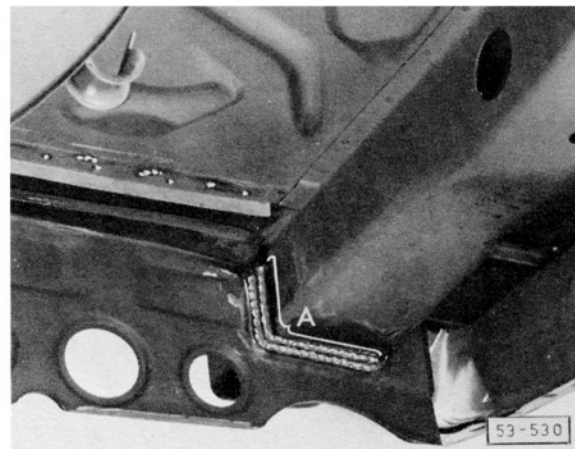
Stoßfängerhalter und Querträger am Abschlußblech einschweißen.
